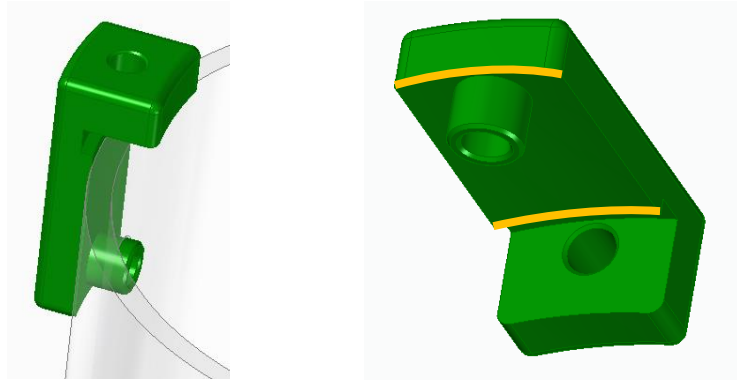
Oberes Befestigungselemente (Geänderter Radius gelb markiert)
